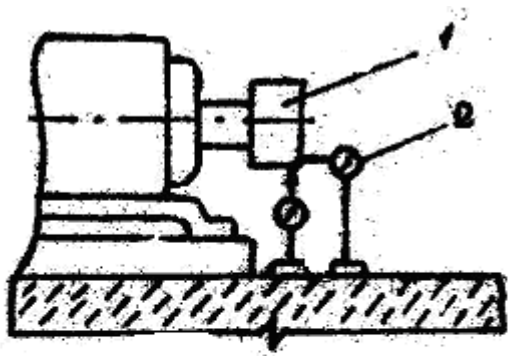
Схема проверки правильности посадки полумуфт На вал: 1- полумуфта; 2-индикатор
